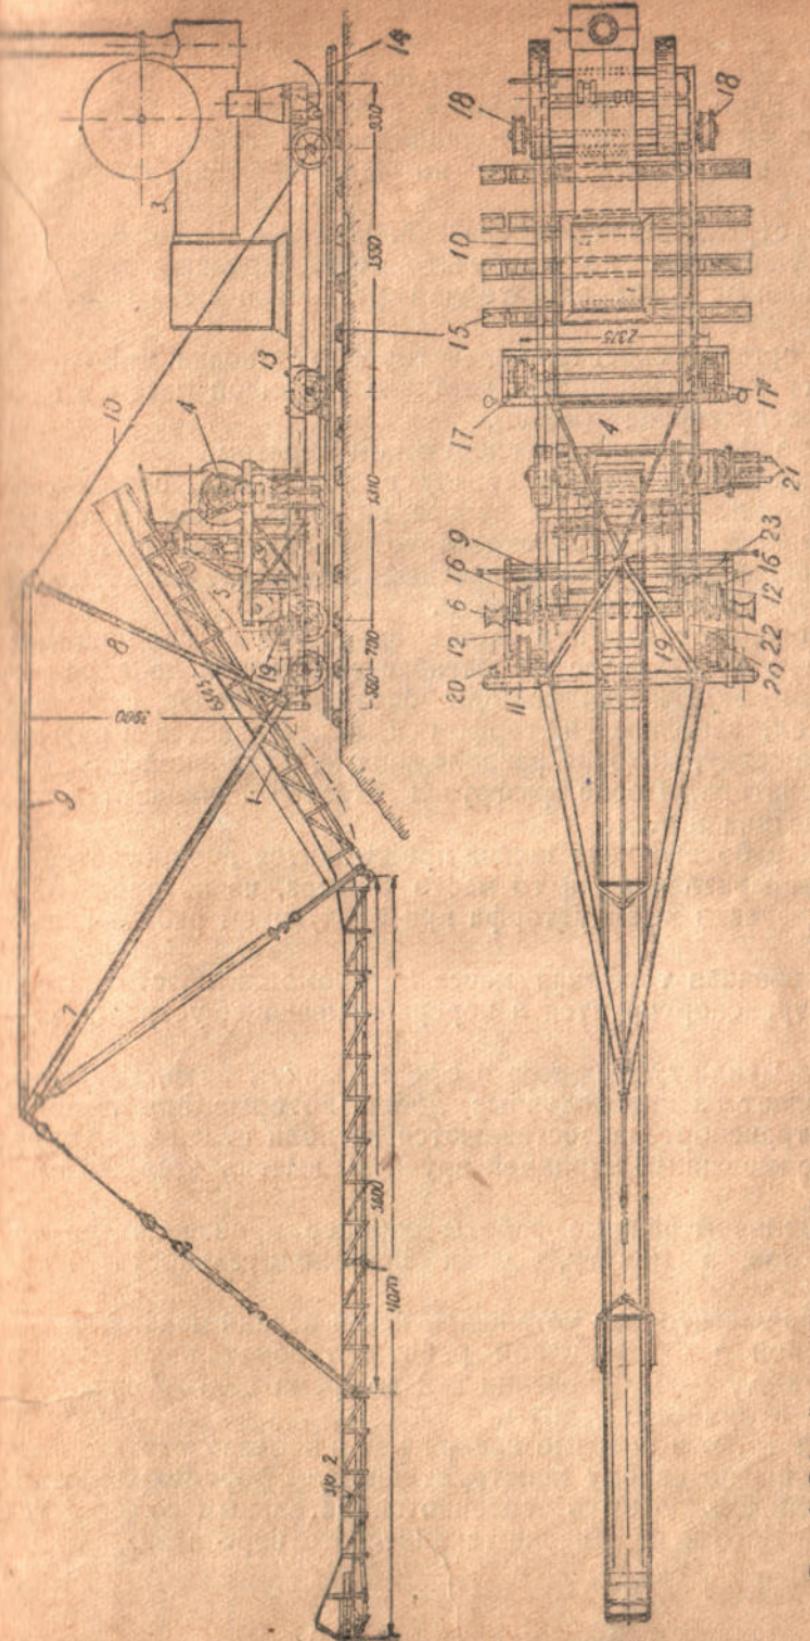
Общий вид элеваторной установки системы Инсторфа (план и боковой вид): 1 — верхнее колено элеватора; 2 — нижнее; 3 — двигатель; 4 — пресс; 5 — козлы; 6 — шпили корневального устройства; 7 — задняя ливунга; 8 — передняя ливунга; 9 — горизонтальная тяга; 10 — наклонная тяга; 11 — попеченные балки; 12 — продольные балки задней рамы; 13 — продольные балки; 14 — рельсы; 15 — шпалы; 16 — колеса третьей пары; 17 — колеса второй пары; 18 — колеса первой пары; 19 — вал шпилевой; 20 — вал шпилевой; 21 — балки головной части транспортера; 22 — 23 — зубчатая передача на шпилевой вал.
